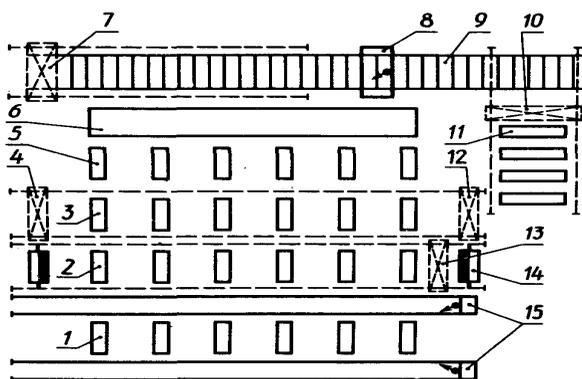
Поточная линия изготовления балок корычато-го сечения:
